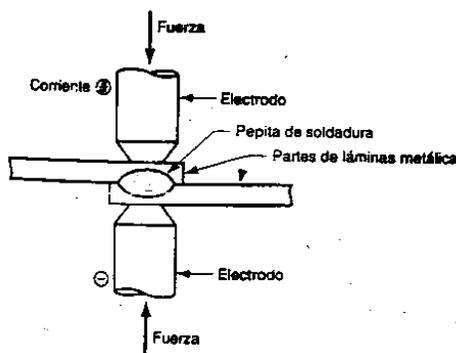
Componentes de la soldadura por resistencia; (fuente: [1], p. 716)
